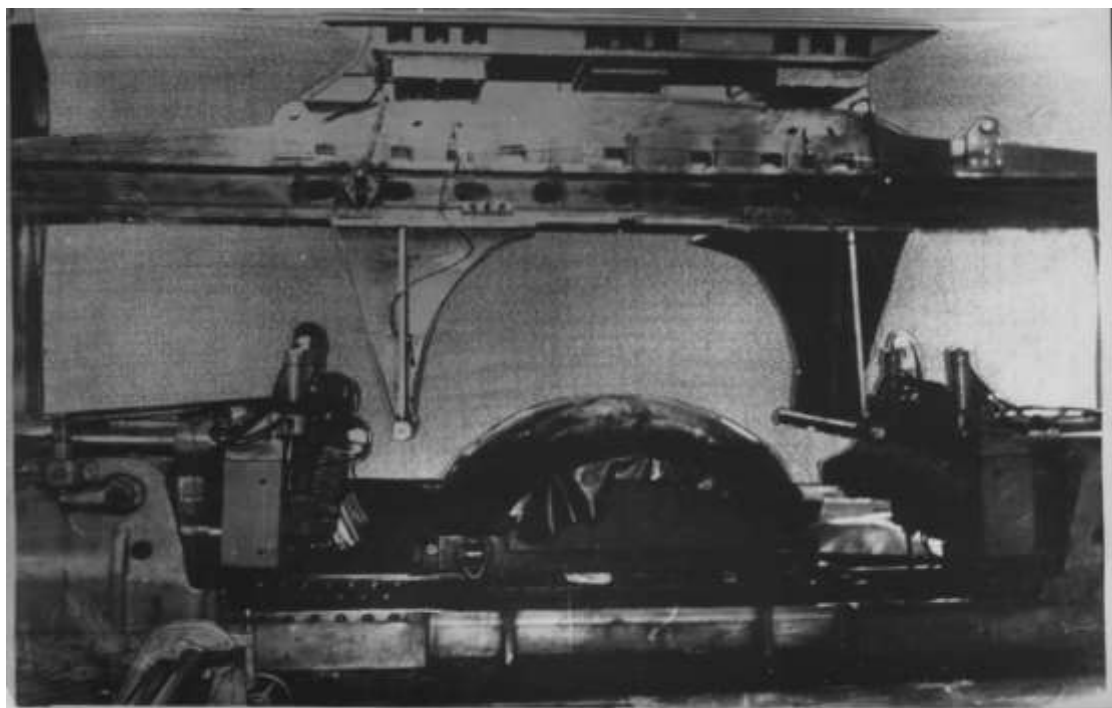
Обтяжной пресс РО-3М, приспособленный для формообразования обтяжкой элемента-осьмушки полусферической оболочки радиуса $R=5180$ мм при размерах заготовки $4000 \times 2100 \times 4,5$ (мм×мм×мм) из свариваемого алюминиевого сплава АМг6М
